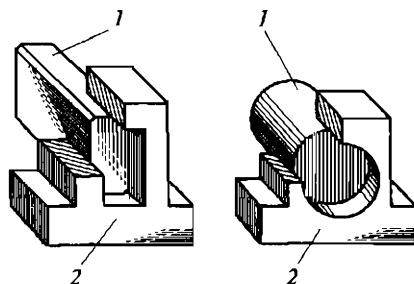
Охватываемые и охватывающие элементы деталей:
